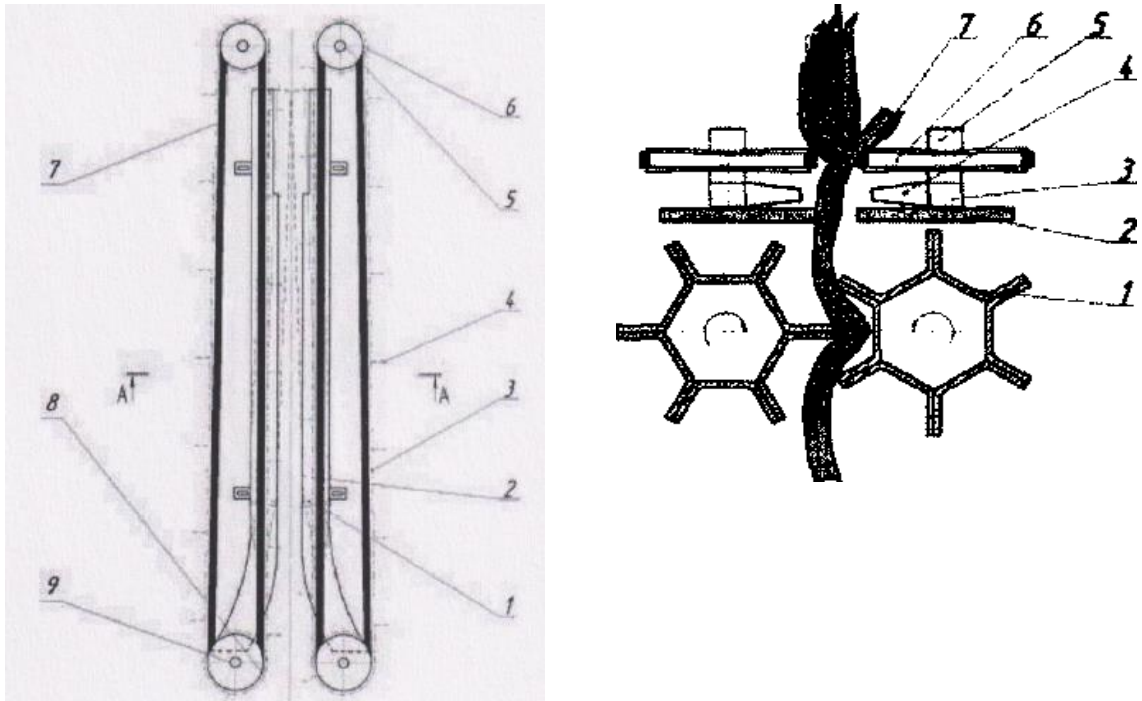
Качановідокремлювальний апарат: а - вид зверху; б – розріз А-А: 1 - протягувальний валець; 2 - качановідокремлювальна пластика; 3 - подавальний ланцюг, 4 - лапка ланцюга; 5 - вал; 6 - ведучий шків; 7 - ремінь; 8 - ведений шків; 9 – вісь.
